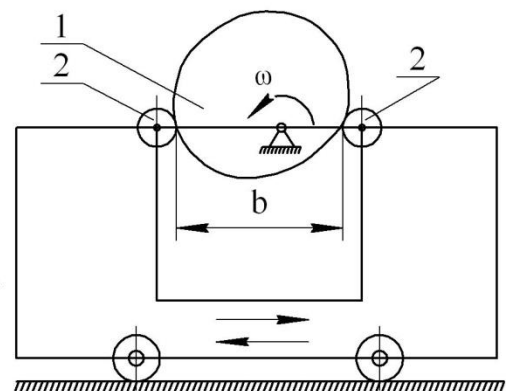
Схема механізму з кулачковим приводом зворотно-поступального руху візка.
